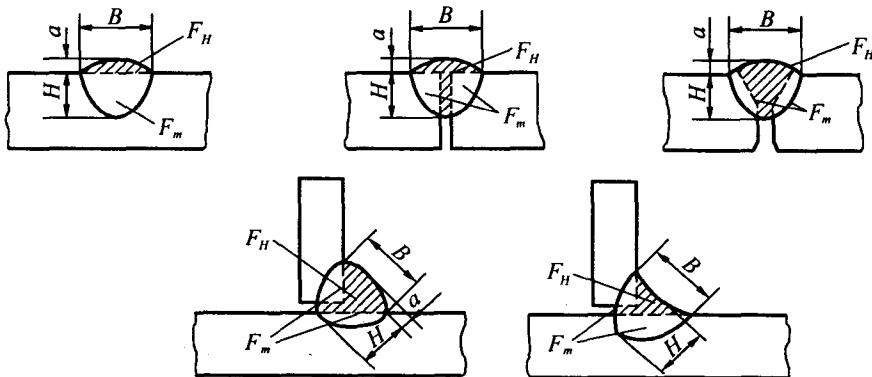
焊缝的形状和尺寸示意图
